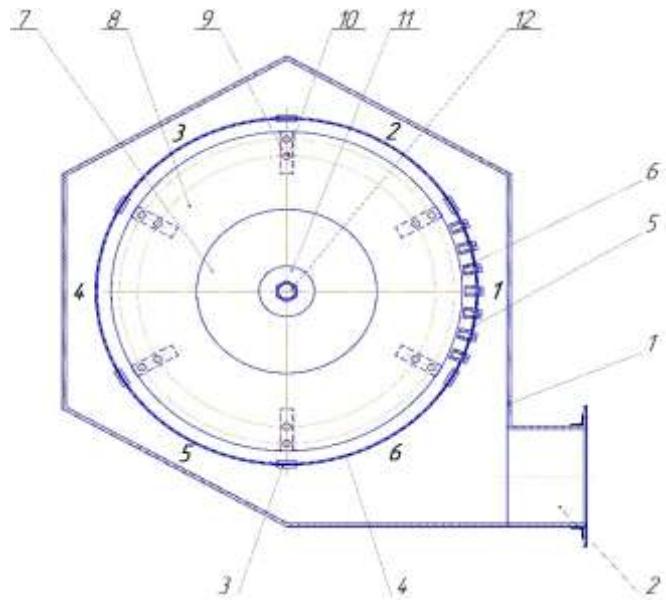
Схема расположения рабочих органов в корпусе камеры измельчения
